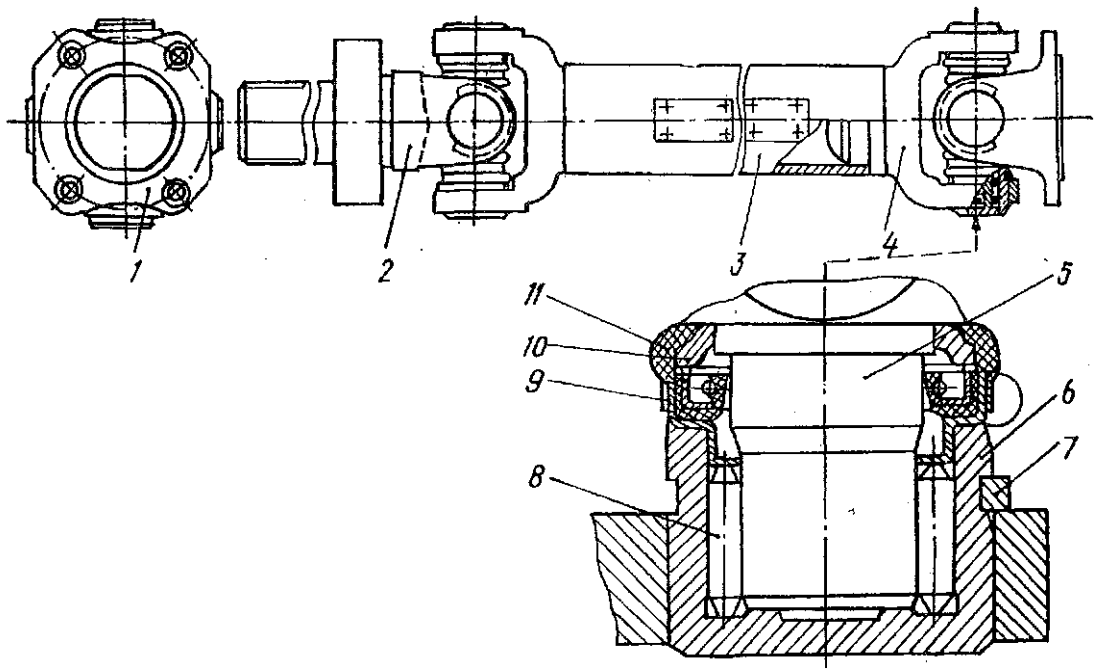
Карданний вал: 1 - фланець; 2 - вилка ковзна; 3 - вал; 4 - вилка; 5 - хрестовина; 6 - обойма голчастого підшипника; 7 - кільце стопорне; 8 - голки підшипника; 9 - манжета ущільнювальна; 10 - відбивач; 11 - муфта захисна.
